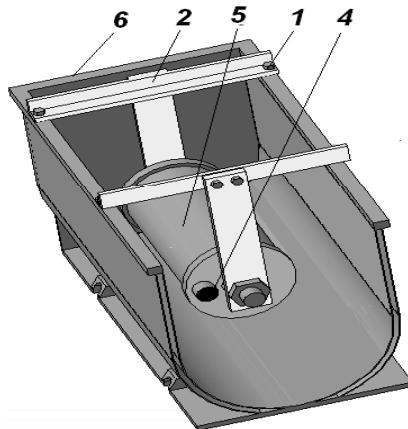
Конструкция рабочей камеры для вибро-ультразвуковой обработки деталей в свободном состоянии с расположением ультразвукового преобразователя в центре рабочей камеры: 1 — резьбовые соединения; 2 — крепление; 3 — смотровой люк; 4 — штуцер для подачи охлаждающей жидкости; 5 — ультразвуковой преобразователь; 6 — рабочая камера
